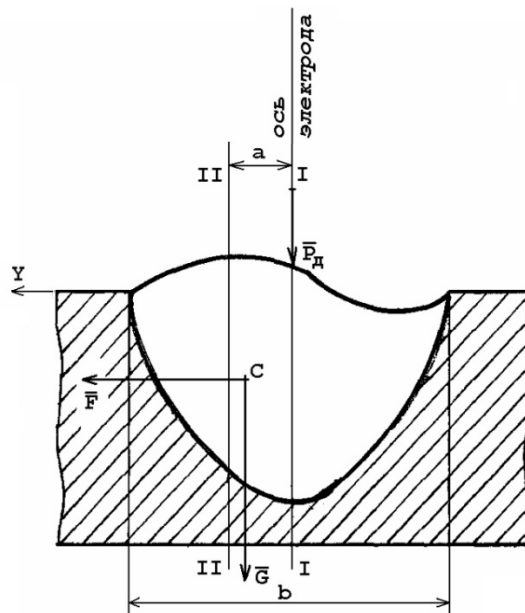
Внешний вид поперечного сечения шва при дуговой сварке в условиях асимметричного поля скоростей; точка C – центр масс поперечного сечения сварного шва
